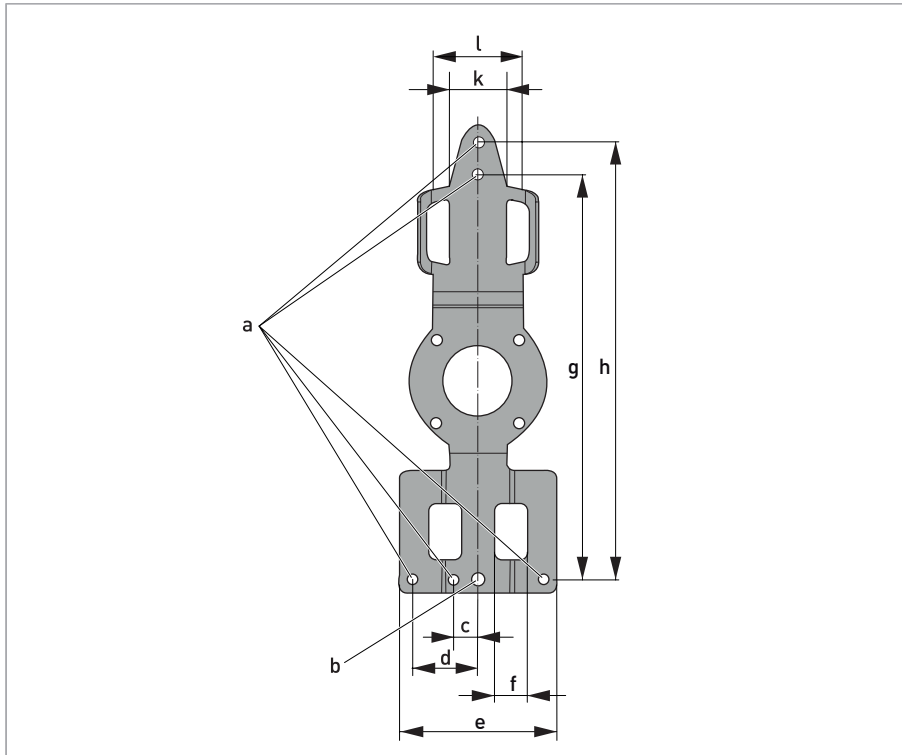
Abmessungen für Montageplatte, Wand-Ausführung
